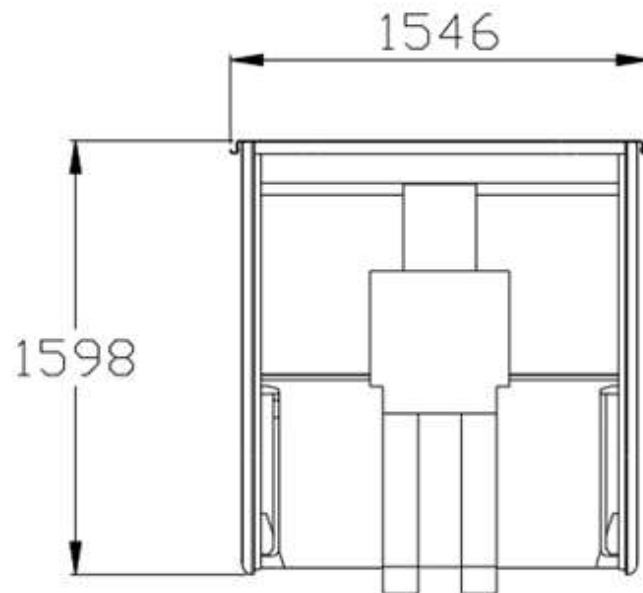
Габаритные размеры кабины (вид спереди)
